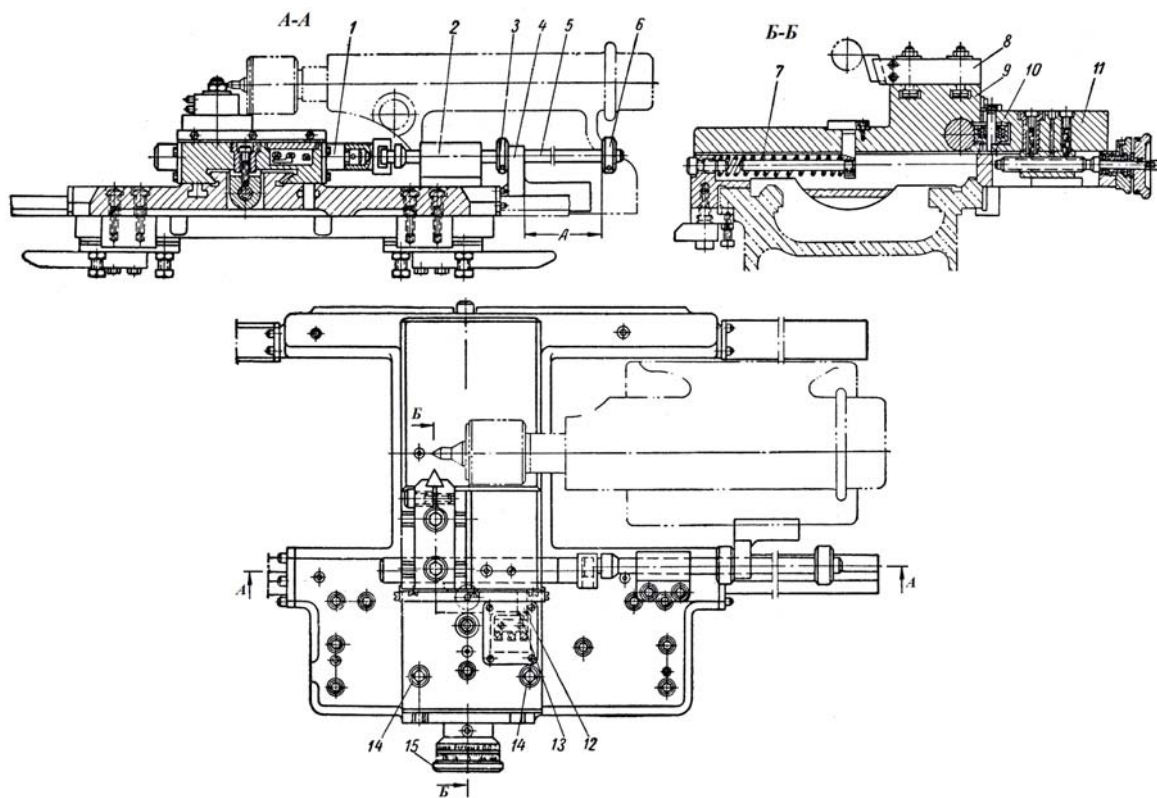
Суппорт токарного полуавтомата мод. КТ-16
